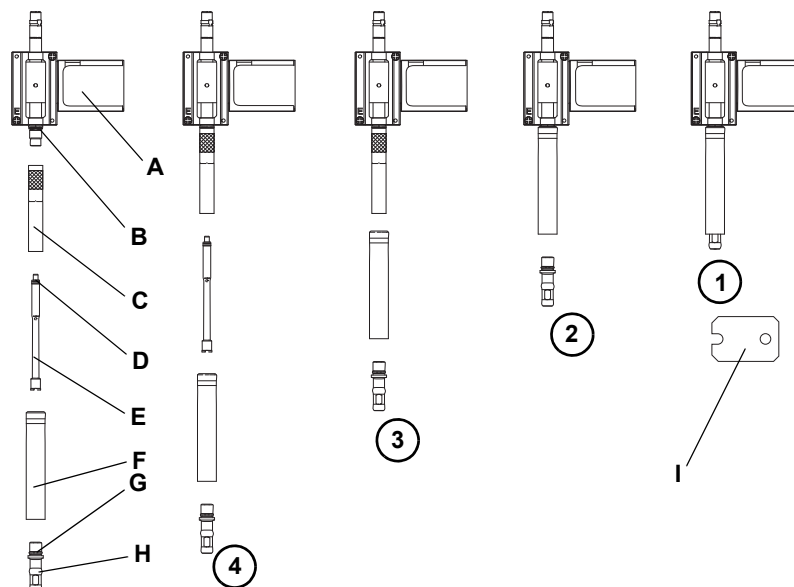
Удаление или установка механизма захвата одноразовых наконечников пневматического устройства LiNa
